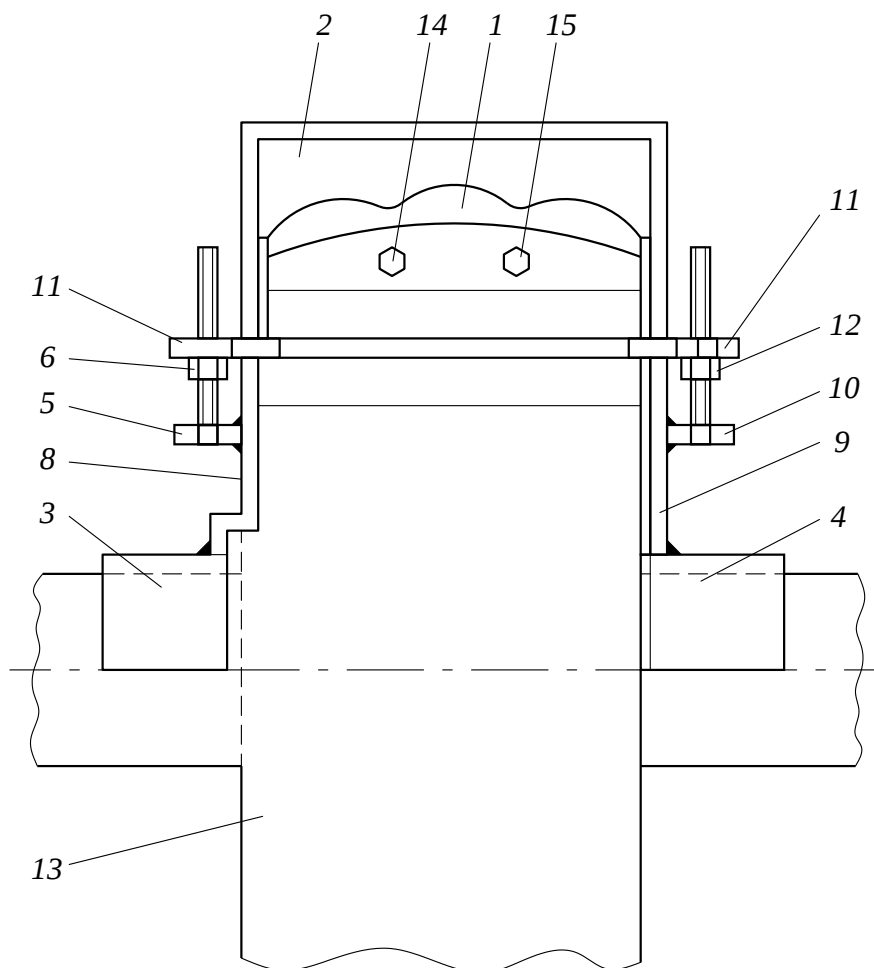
Устройство для установки разбивочных ножей на рабочий барабан
